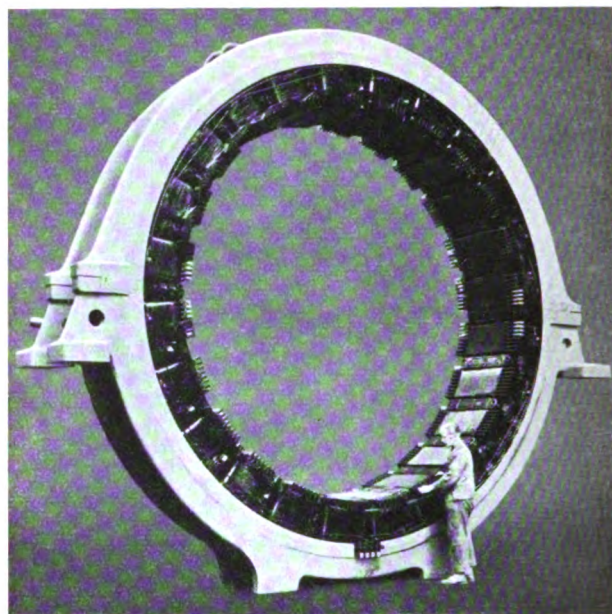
Fördermotor, 4025 kW,  $\pm 850$  V, 58,6 U/min.
